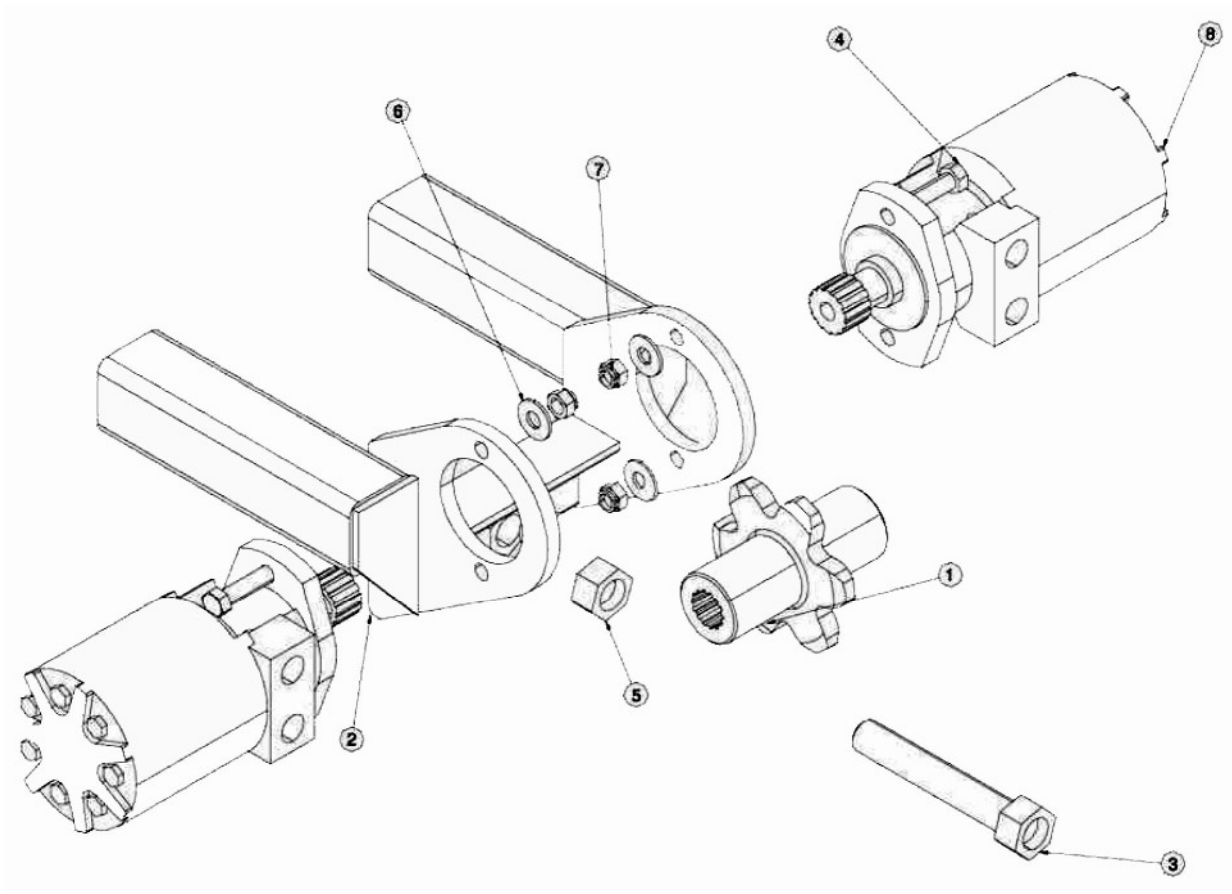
Чертеж сборки двигателя толкателя - A8011-00
